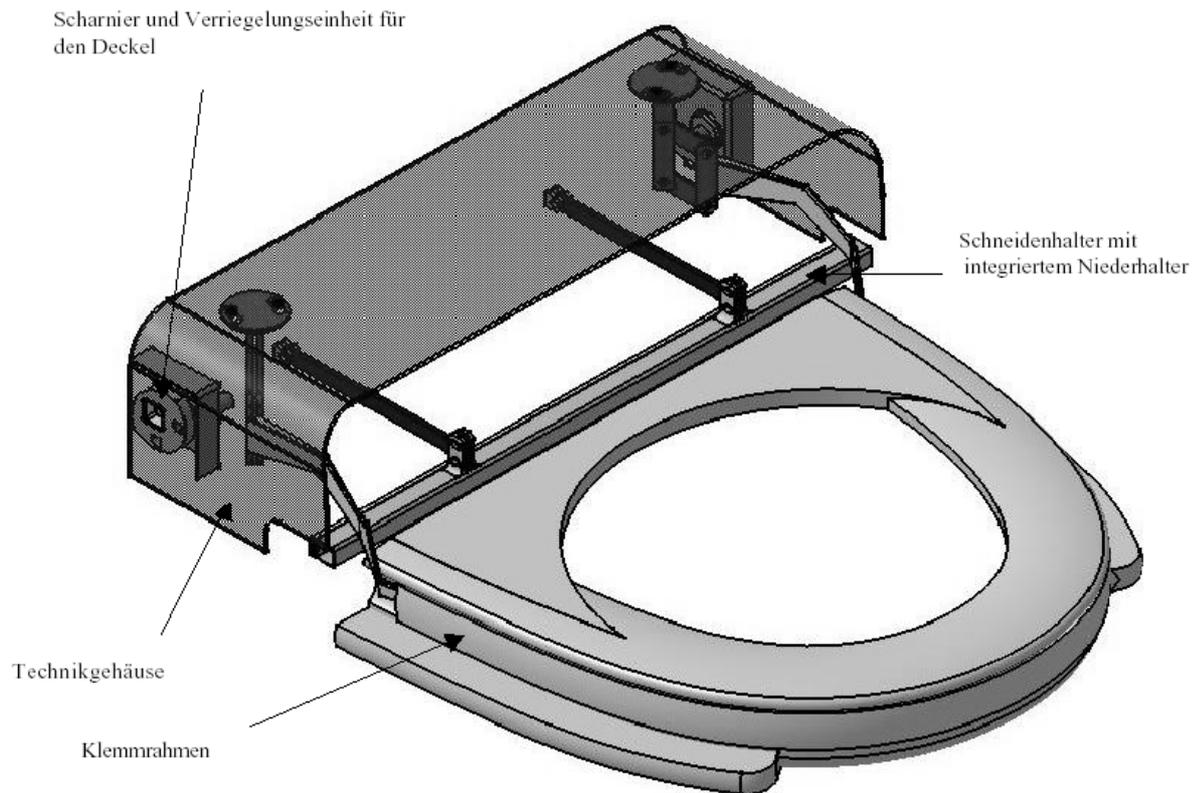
Technikgehäuse mit Toilettenbrille
